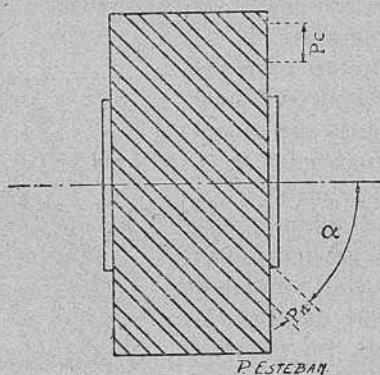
Manera de tomar el P_c y el P_a en un engranaje helicoidal.
